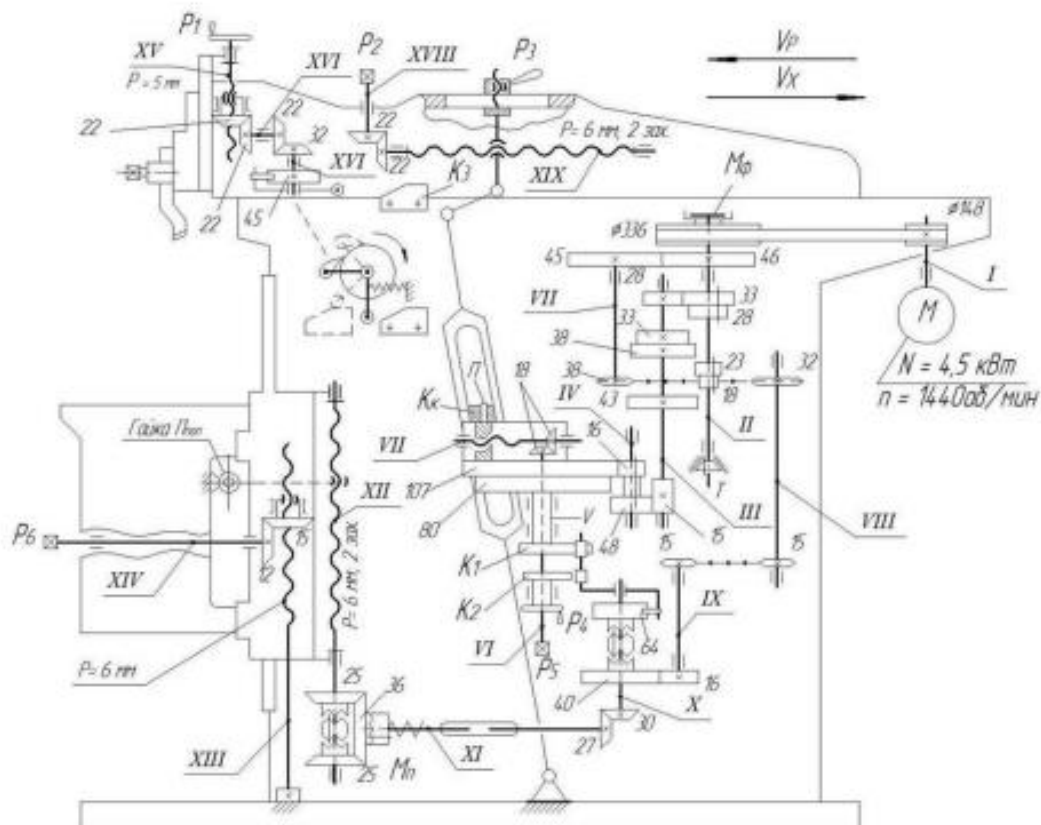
Кинематическая схема поперечно-строгального станка 7Б35
